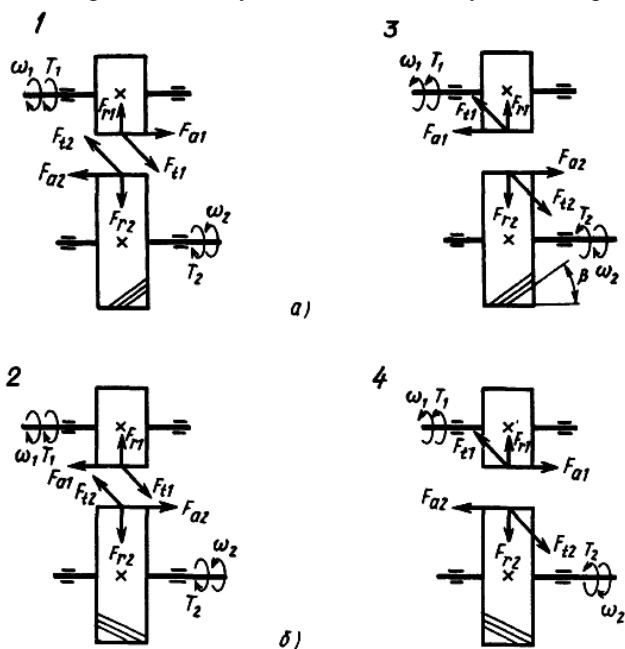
Схема сил в зацеплении косозубой цилиндрической передачи: а – направление линии зуба колеса – левое, шестерни – правое, б – колеса – правое, шестерни – левое. Схемы 1, 2 – вращение быстроходного вала по часовой стрелке, схемы 3, 4 – против часовой стрелки (смотреть слева).
